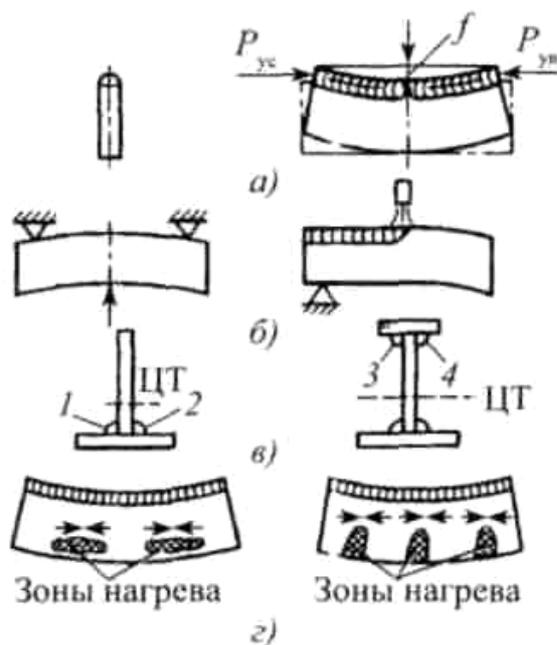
Деформация изгиба сварных заготовок и способы ее устранения
